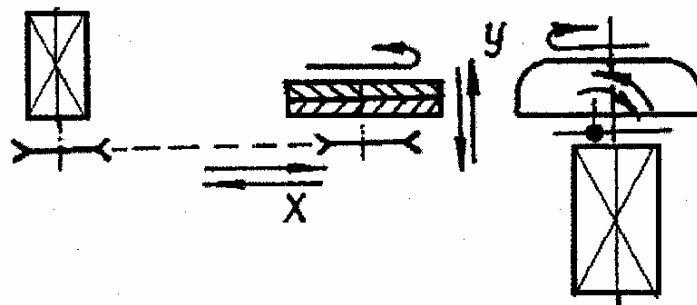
Схема движений инструмента и детали в процессе обработки поверхности (X, Y – направления движений инструмента и детали)
